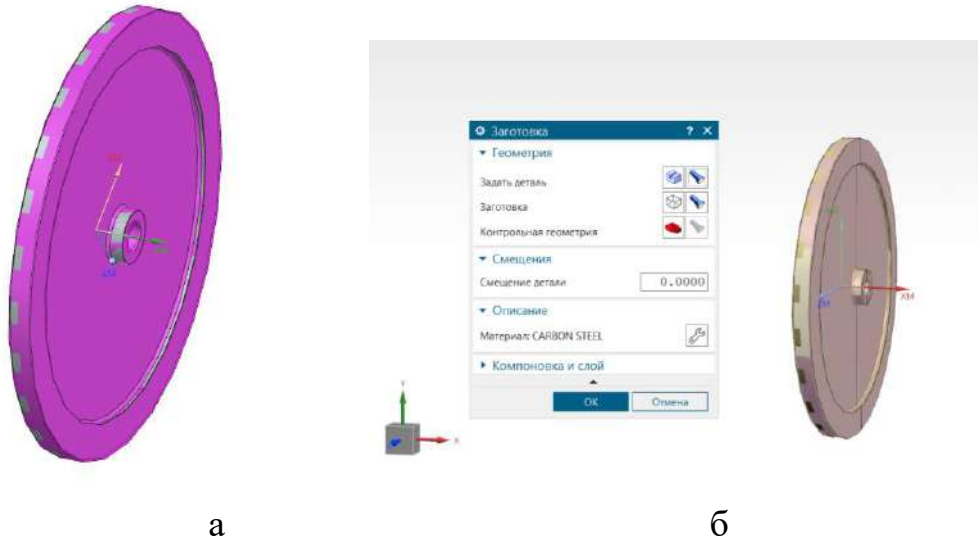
Поєднання (а) зображення та визначення (б) деталі з заготовкою в системі NX CAM
